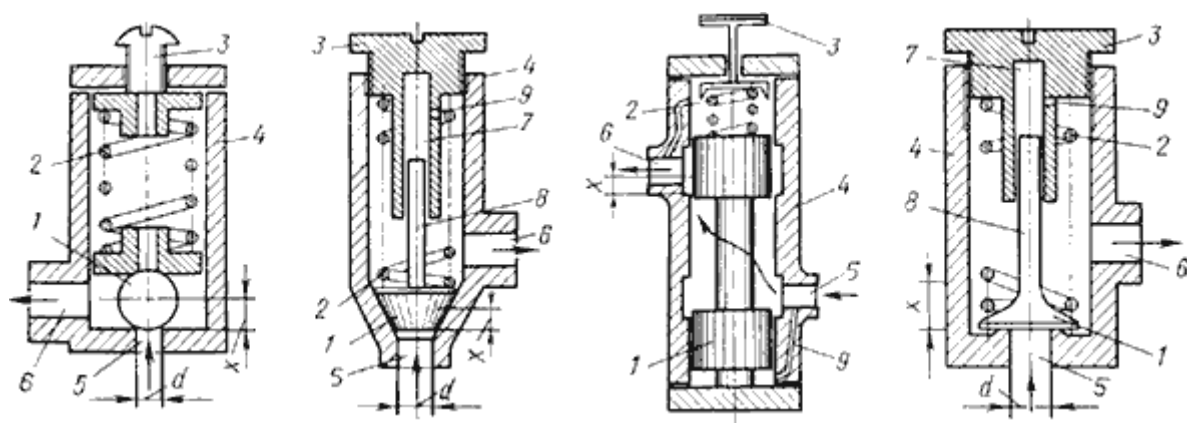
Принципиальные схемы напорных клапанов с запорно-регулирующими элементами: а - с шариковым; б - с конусным; в - с золотниковым; г - с тарельчатым
